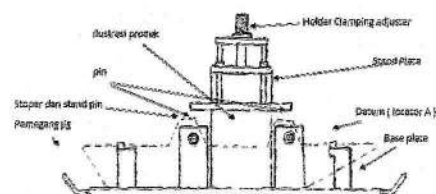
Alternatif Konsep 1 Jig – Check Fixture BCSB D-17
